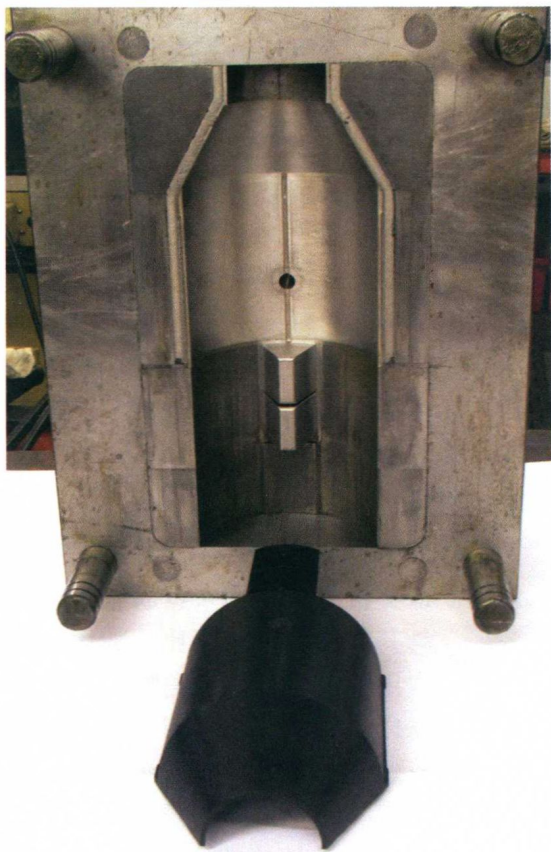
一个机械加工的半模和由该模具生产的塑料件
